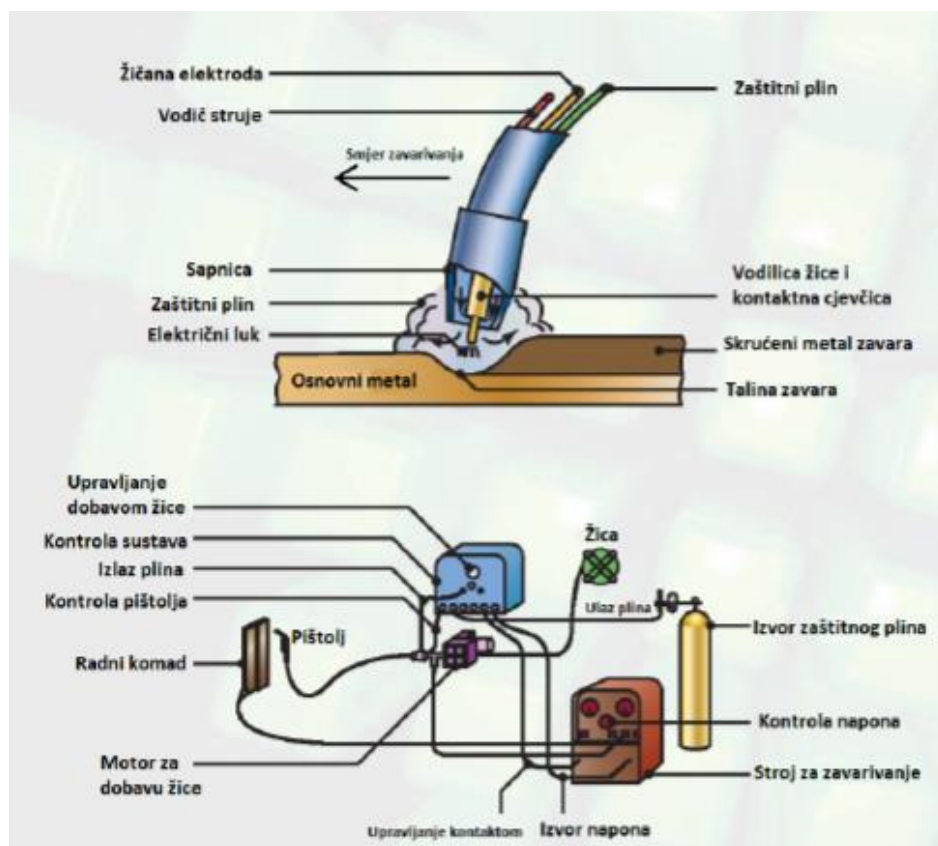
Shematski prikaz MIG zavarivanja [10]
